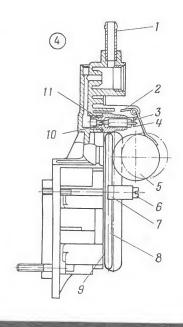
Так проверяют уровень топлива и свободный ход поплавка: 1 — штуцер; 2 — упор; 3 — шарик демпфирующего устройства; 4 — язычок; 5 — поплавок; 6 — винт; 7 — прижиминая планка; 8 — стержень; 9 — прокладка; 10 — игла; 11 — седло
